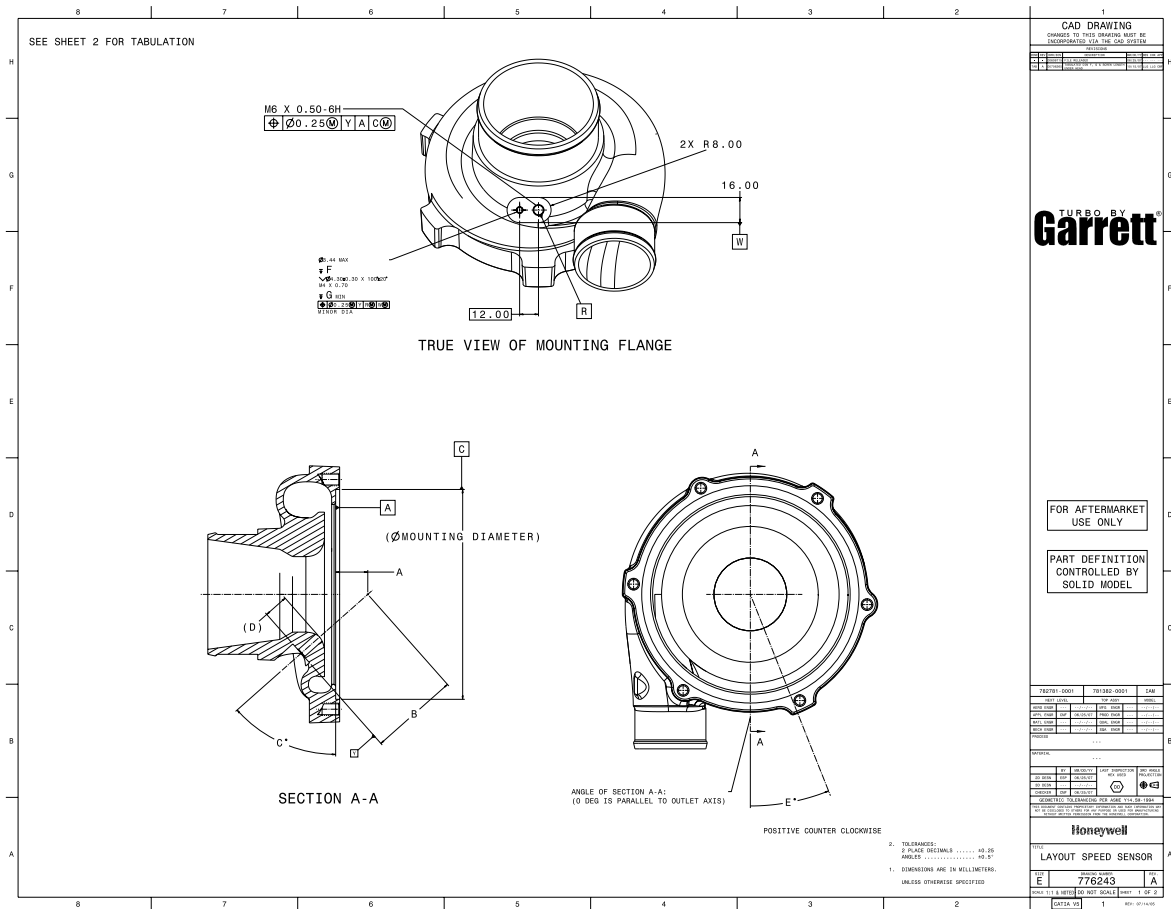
Desenho técnico da instalação do sensor de velocidade de rotação do turbocompressor (Speed sensor Garrett, 2012).
